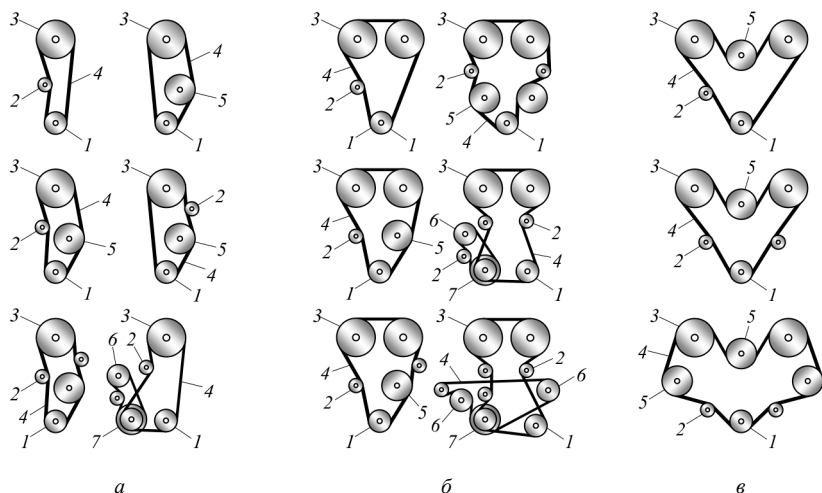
Основные схемы ременного привода механизмов: а – двигателя с одним верхним распределительным валом; б – двигателя с двумя верхними распределительными валами; в – V-образного двигателя с двумя верхними распределительными валами; 1 – шкив коленчатого вала; 2 – натяжные и (или) паразитные ролики; 3 – шкив распределительного вала; 4 – ремень; 5 – шкив вала вспомогательных механизмов; 6 – шкив алансирного вала; 7 – шкив генератора
